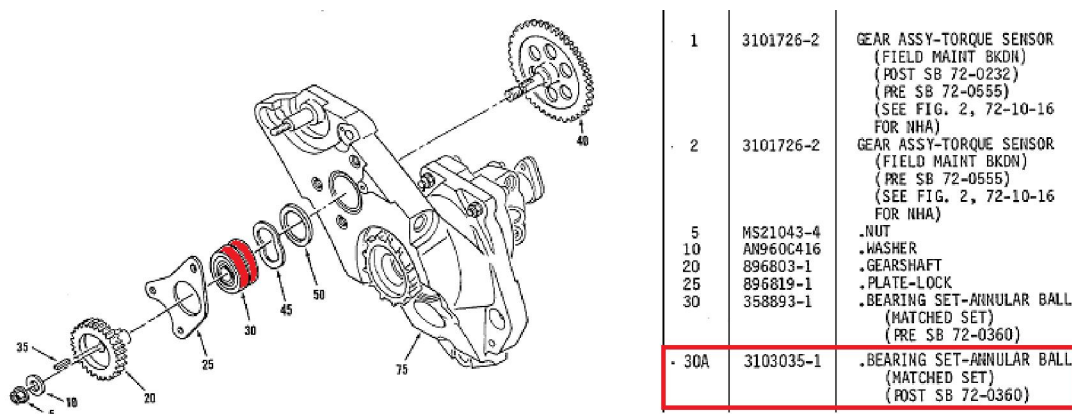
Ensamblaje del sensor de torque posterior a la aplicación del SB 72-0232 y previo al SB 72-0555 (resaltado en rojo sobre el dibujo la primer versión del rodamiento en cuestión, recuadrado en rojo sobre la tabla la versión posterior al SB 72-0360).
